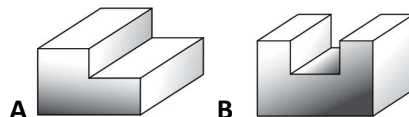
A: Fresagem lateral (*Side Milling*); B: Fresagem “em cheio” (*Slotting*)
